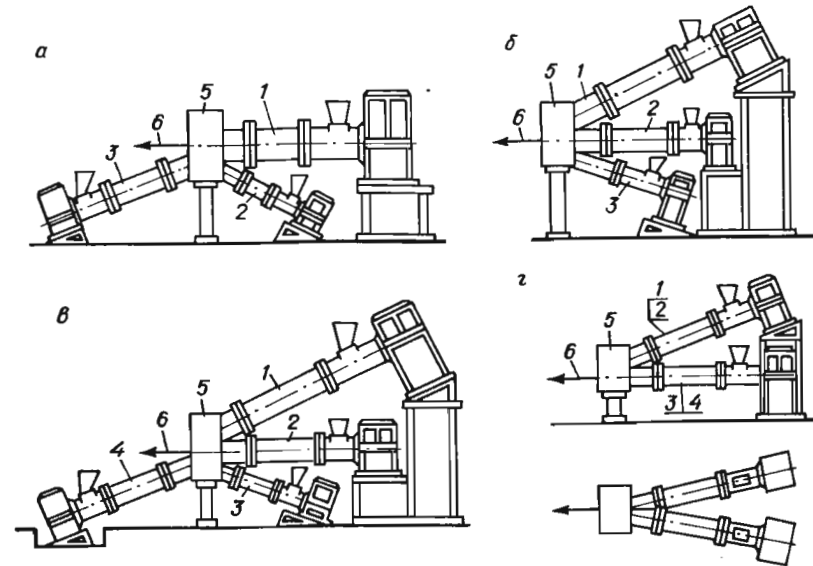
Варианты агрегирования трех (а, б) или четырех (в, г) червячных прессов для профилирования многослойных заготовок: 1—4 — червячные presses; 5 — головка; 6 — направление отбора заготовок
